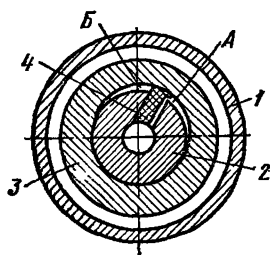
Схема планетарного вибровозбудителя пневматического вибратора:
